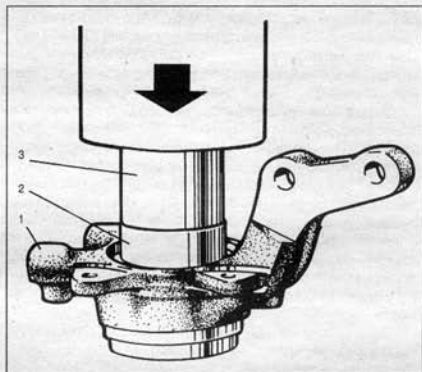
Запрессовка подшипника в поворотный кулак: 1 – поворотный кулак; 2 – подшипник; 3 – оправка
